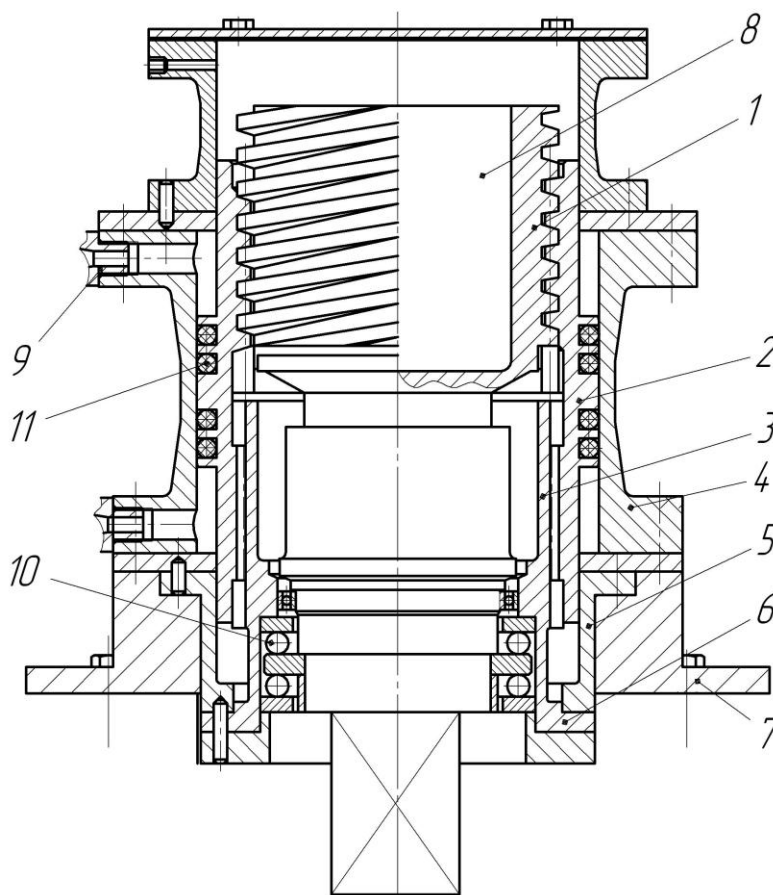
Поворотний гідродвигун поворотний типа гвинтова пара робочого обладнання автогрейдера.
